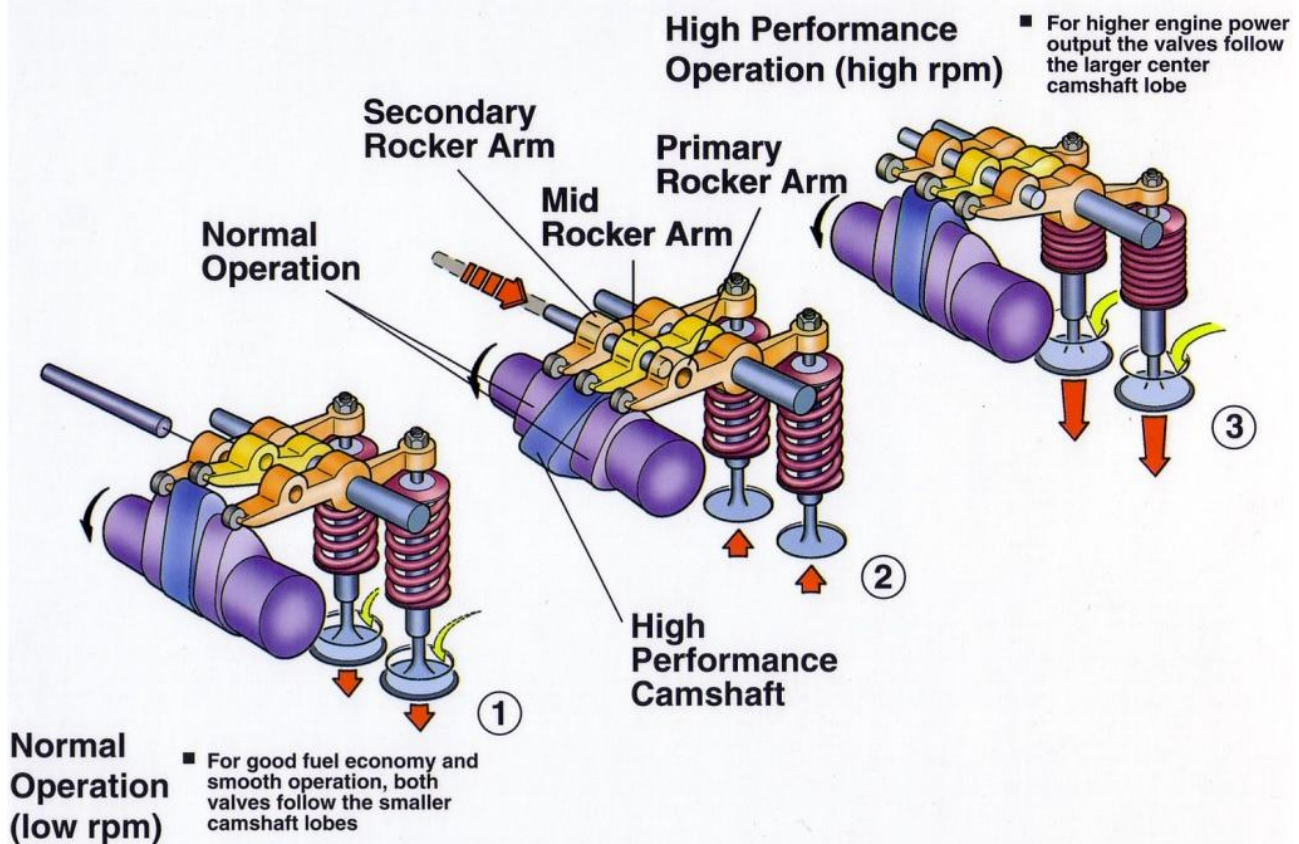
Schema di funzionamento del sistema VTEC Honda. Si notano le camme a bassa alzata, quella ad alzata elevata e il perno di accoppiamento. [7]
